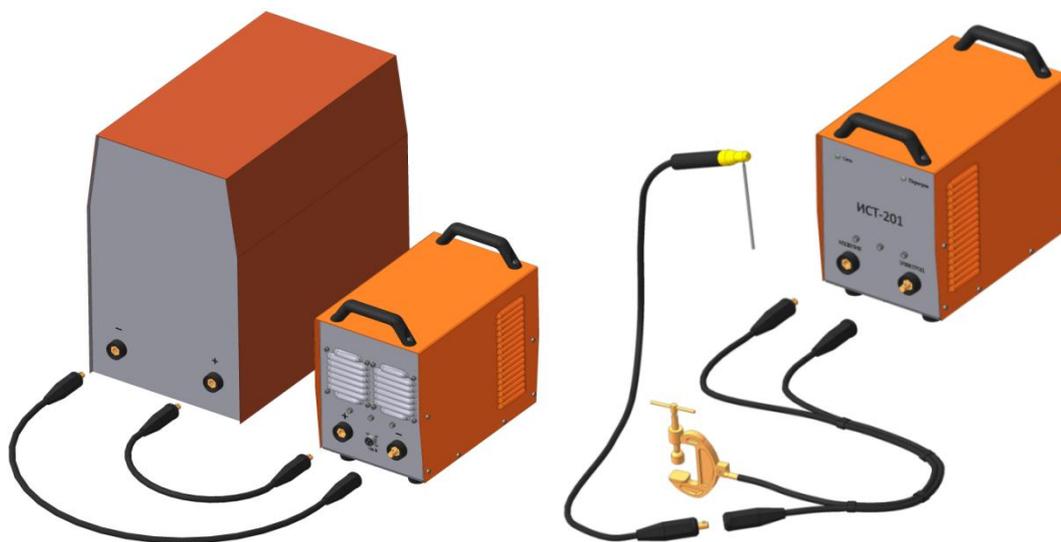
Внешний вид и схема подключения инвертора сварочного тока ИСТ-201
